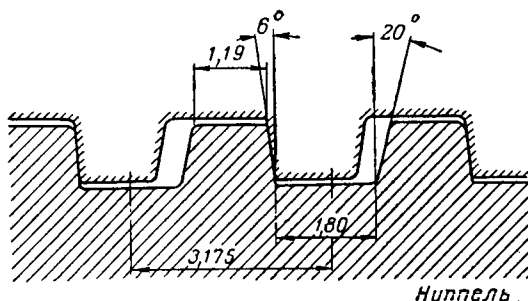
Профиль резьбового соединения «Хайдрил» (профиль резьбы 8 ниток на 1').
